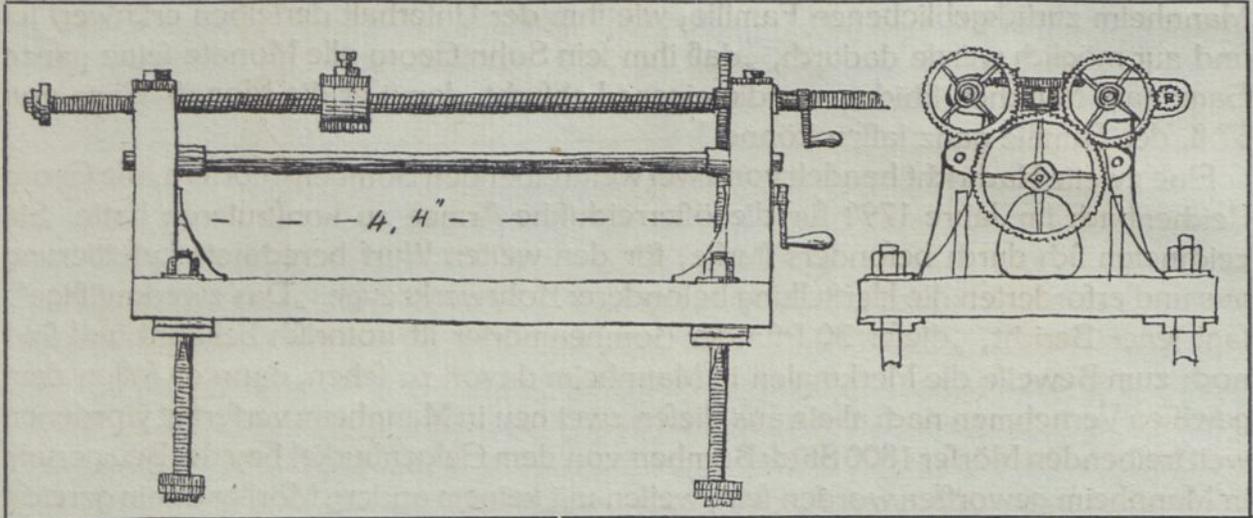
Skizze der Bohrmaschine für das Wiener Bohrhaus.
